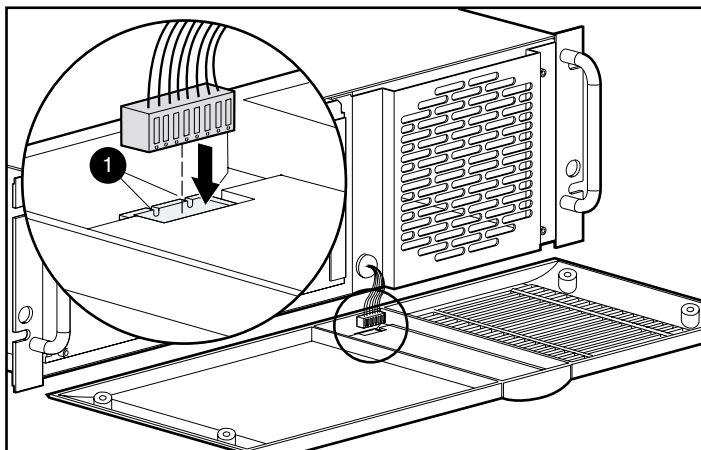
Erneutes Einstecken des Kabels der LED-Anzeige
